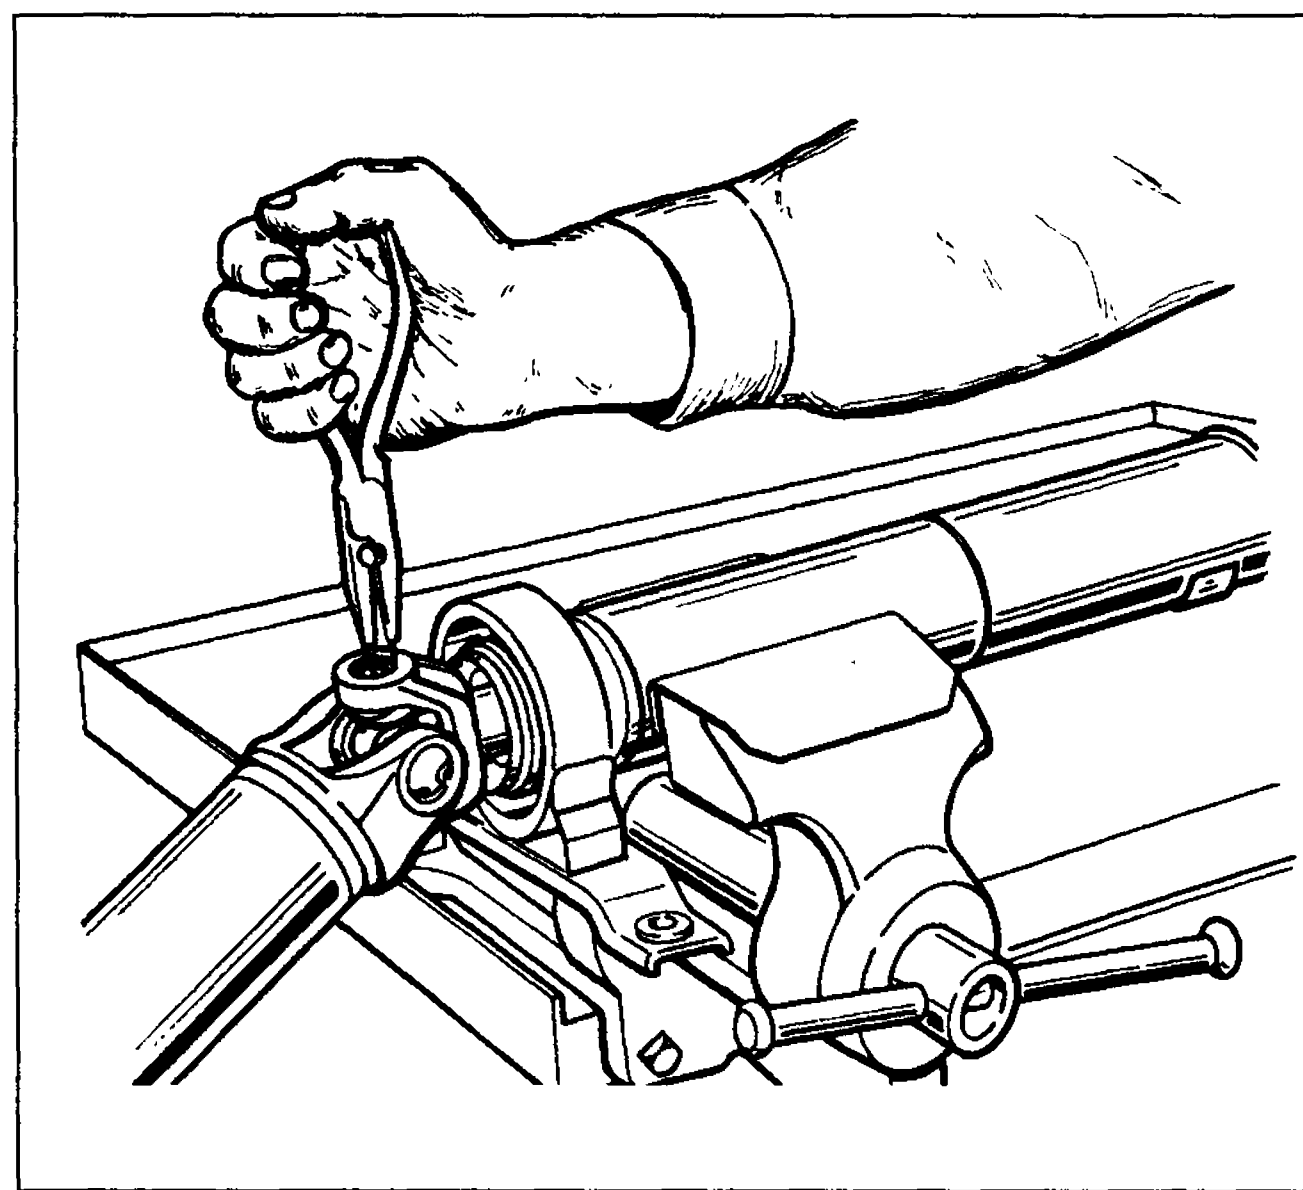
Извлечение стопорных колец подшипников крестовины
